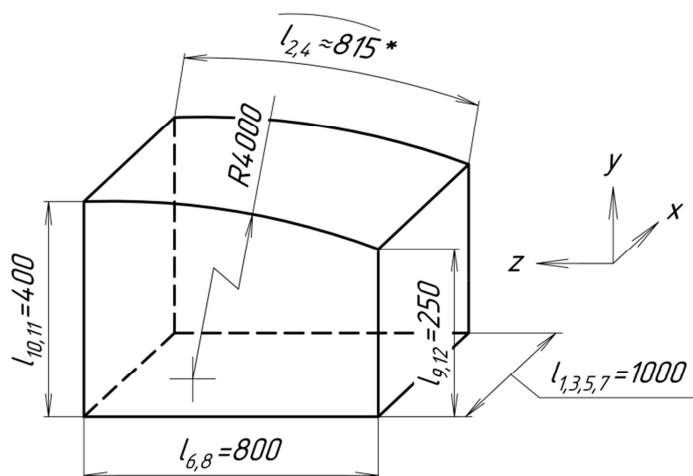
Схема расположения и обозначения элементов каркаса сварного отсека
